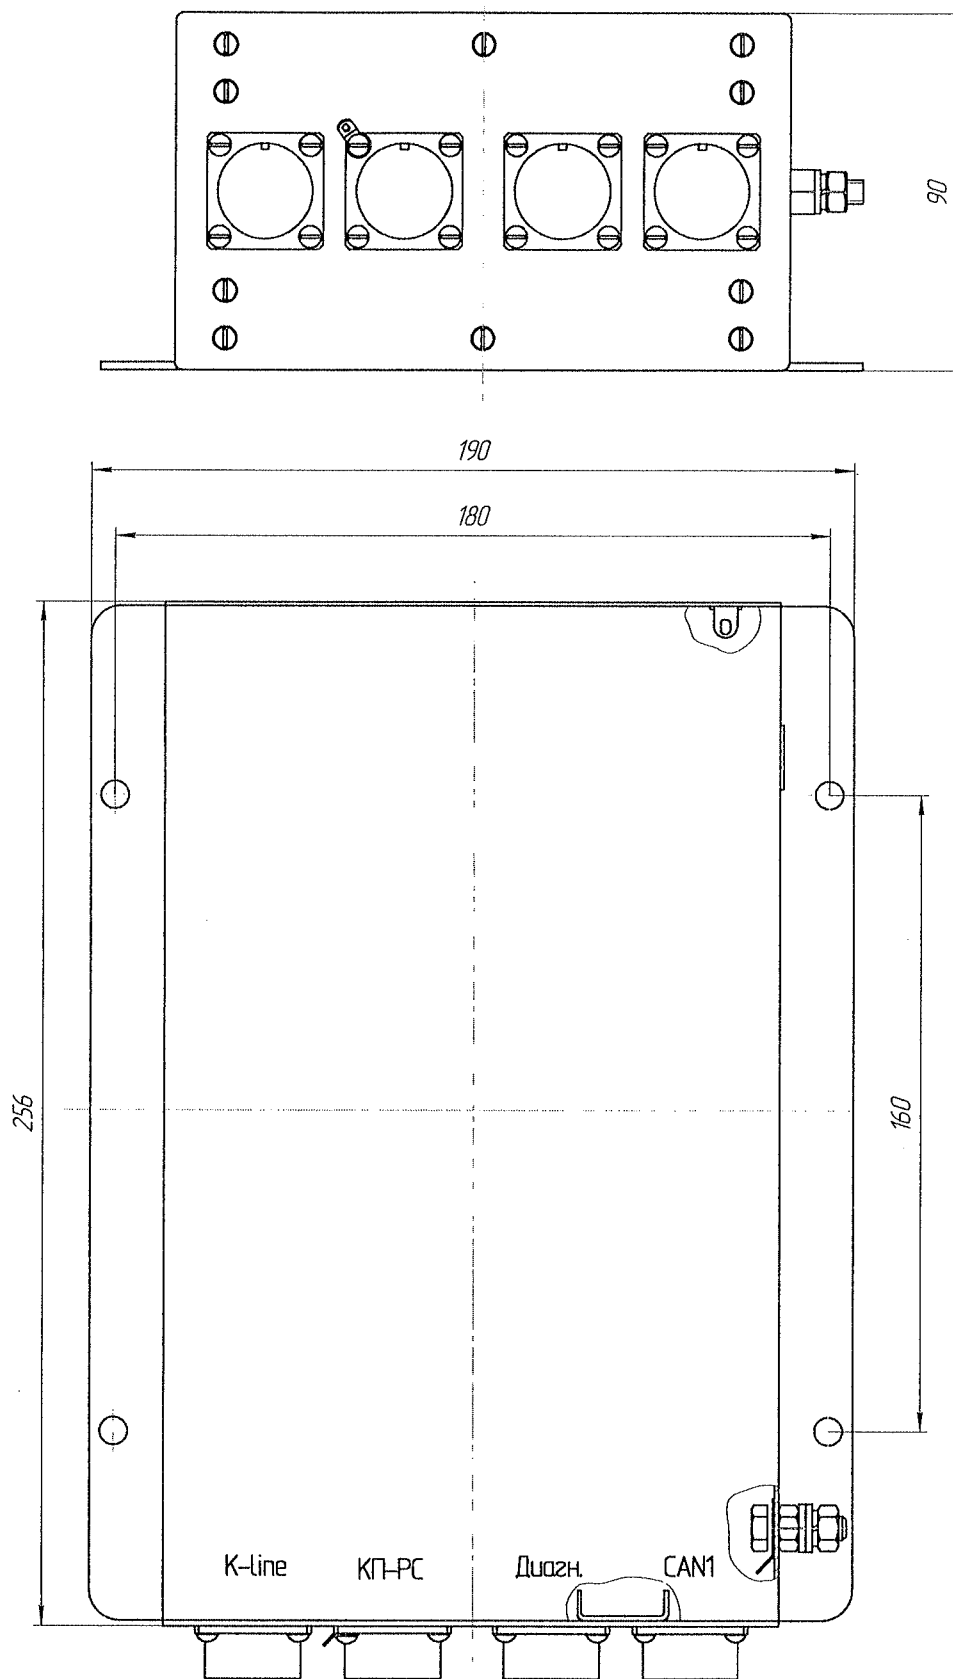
Внешний вид и габаритные размеры блока
